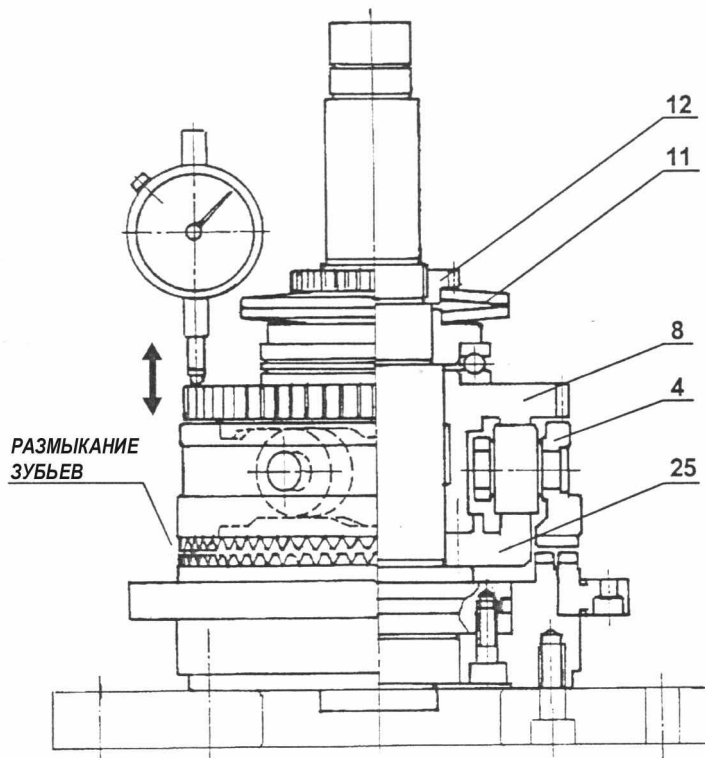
Проверка осевого зазора при сборке кулачкового механизма
